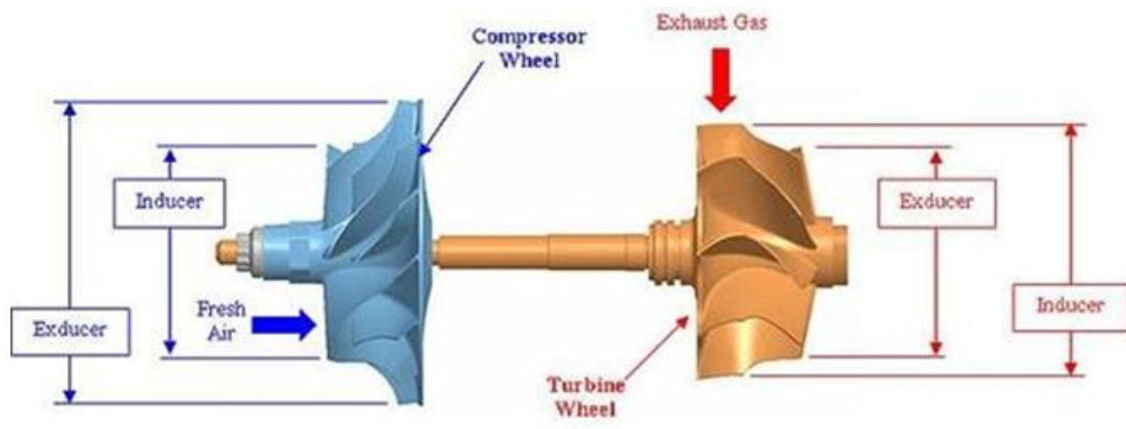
Ajustante (*exducer*) e Amontante (*inducer*) dos rotores do compressor e turbina (Fonte: VTC)
